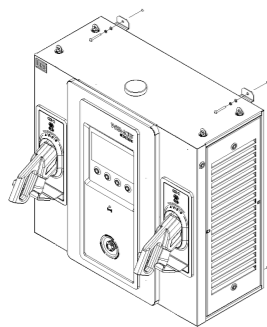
Exemplo fixação da estação WEMOB-STATION (60/80 kW) à estrutura de concreto
